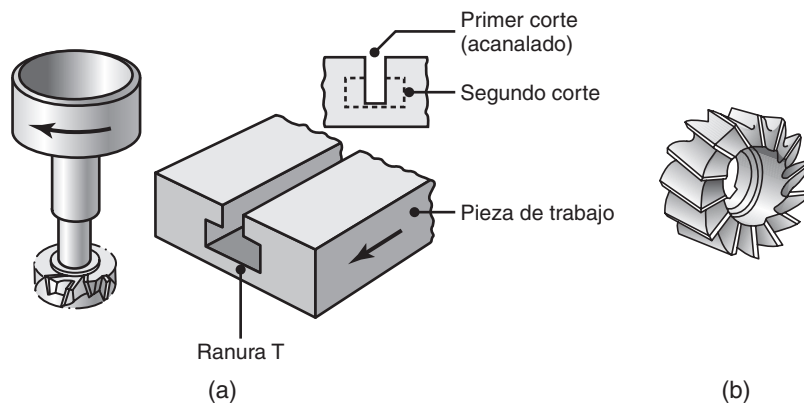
(a) Corte de ranura T con un cortador de fresado. (b) Fresa hueca.
